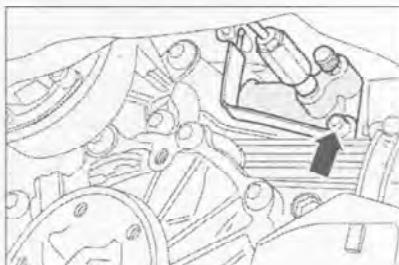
Отверните болт (стрелка), снимите рабочий цилиндр сцепления и закрепите его проволокой.
